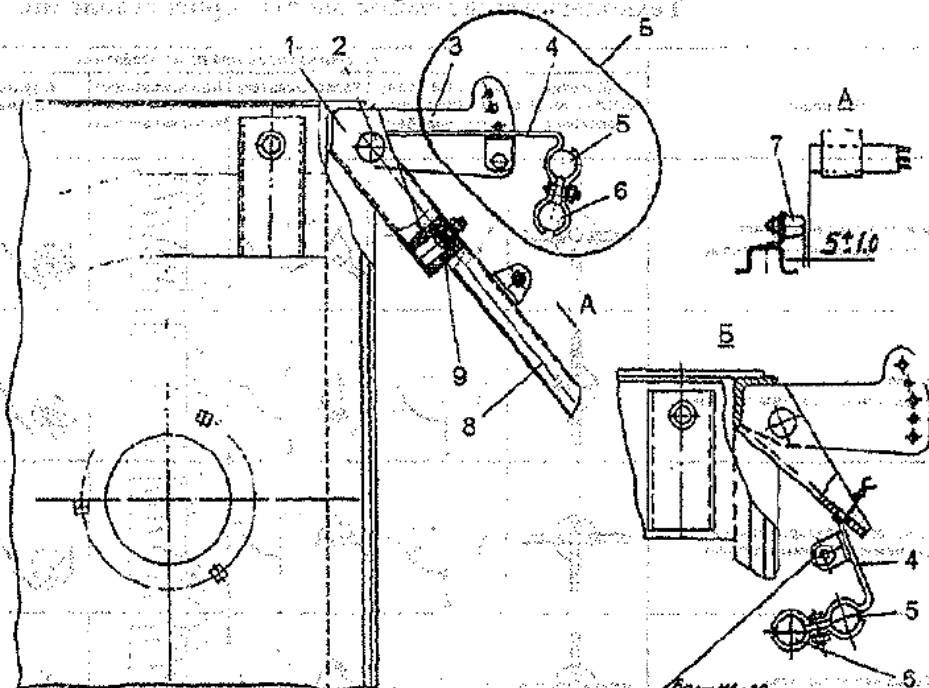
Сигнализатор заполнения копнителя: 1-опора; 2-ось; 3-стойка; 4-скоба; 5, 6-датчики положения; 7-магнит; 8-штанга поворотная; 9-амортизатор
